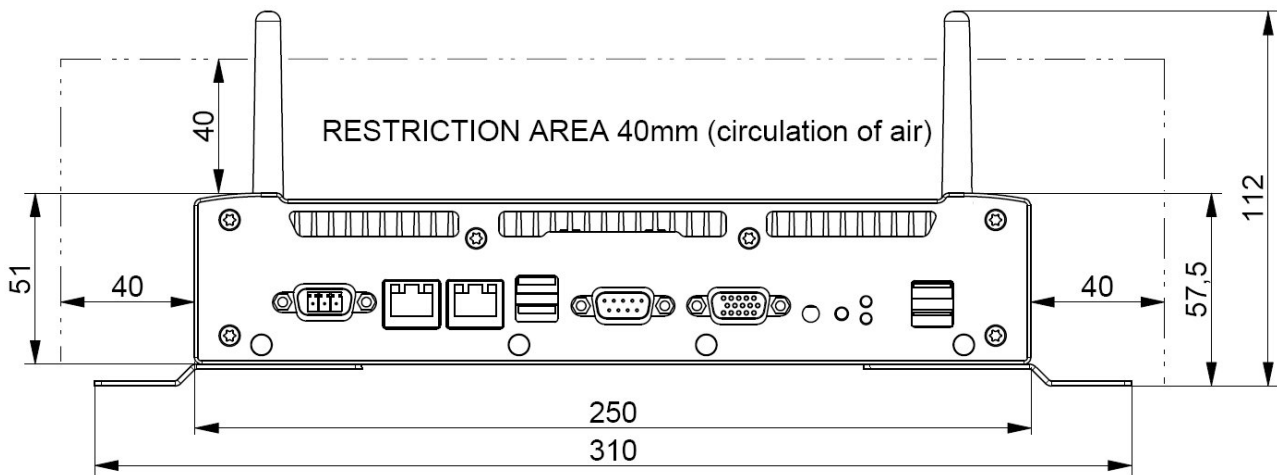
Maßangaben an der Frontansicht (Wand- oder Tischmontage)
